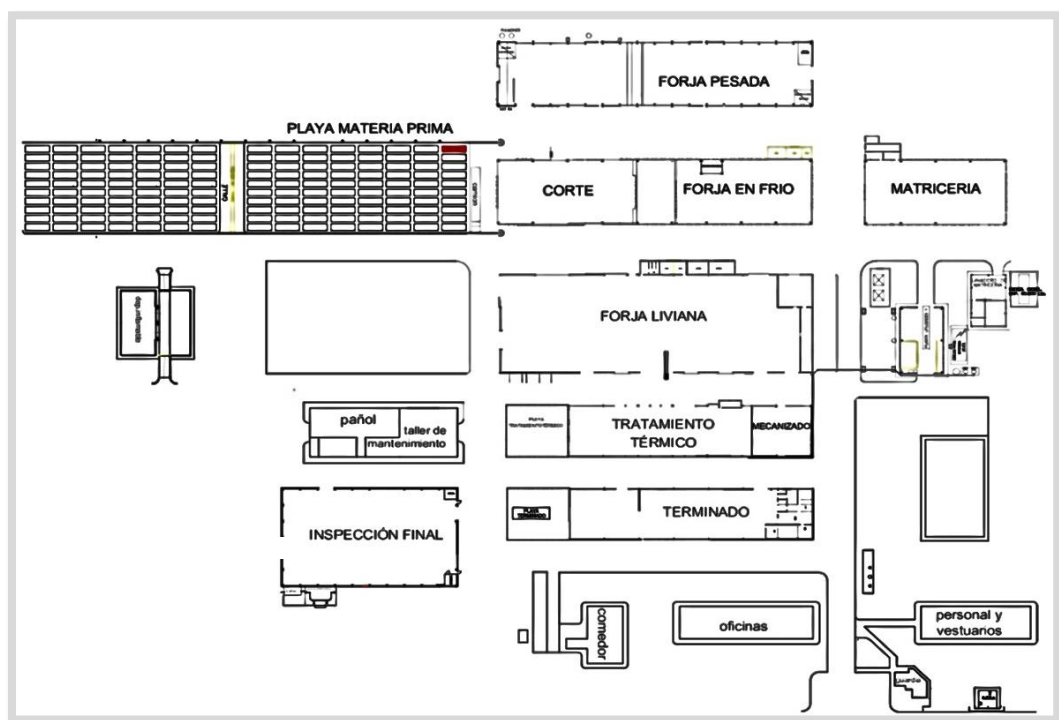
Lay-out de la planta CRAFMSA. Fuente: planos empresa
